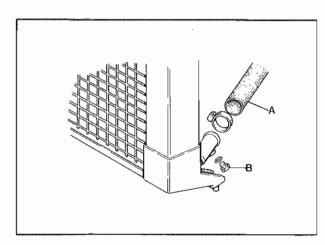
A - Tubo ritorno acqua Coolant return pipe B - Tappo scarico acqua radiatore Radiator coolant drain plug
